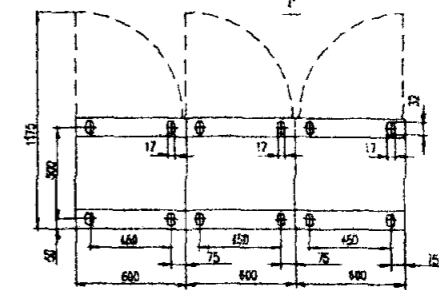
Габаритные, установочные, присоединительные размеры установок КАУ
